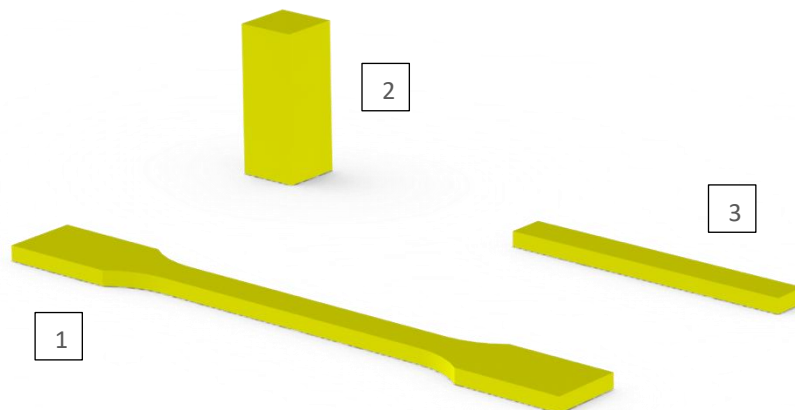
Diseño probetas. 1, Tracción; 2, Compresión; 3, Flexión. Fuente: propia
